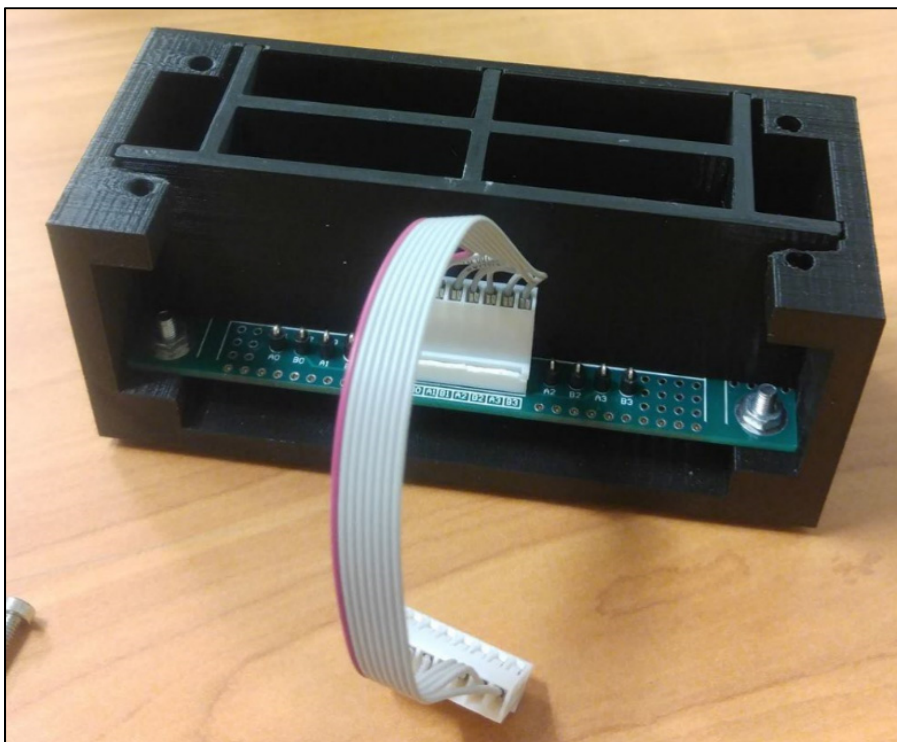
Assemblage du boîtier et du PCB de cellules PV
